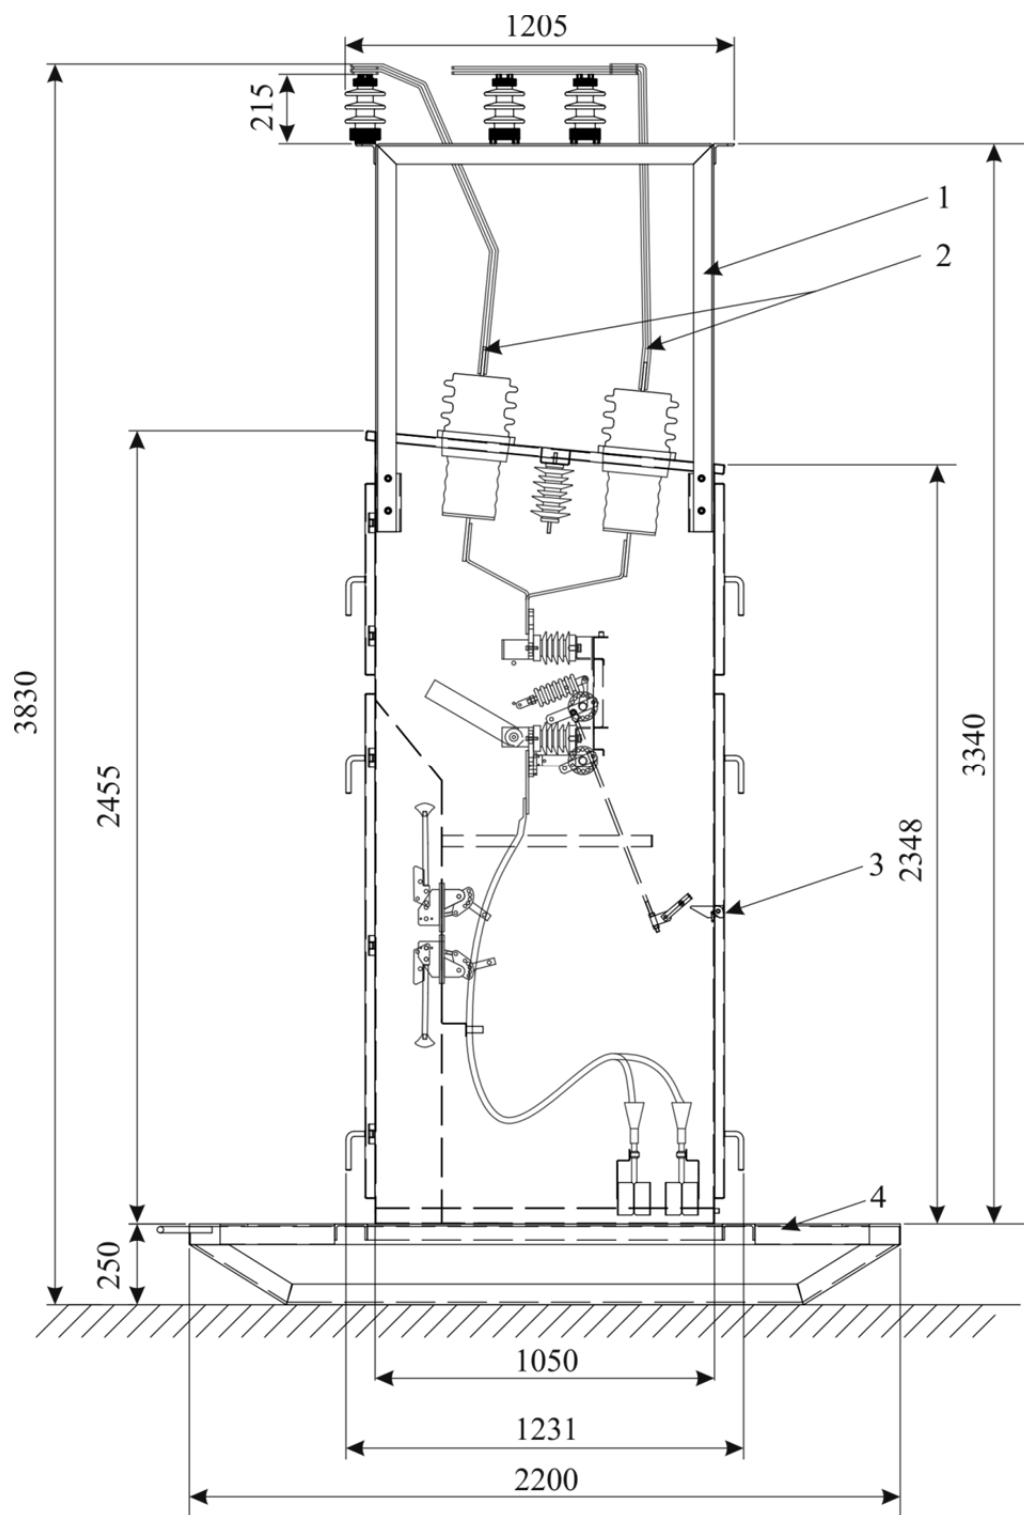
Габаритные размеры и устройство КРН с вакуумным выключателем
